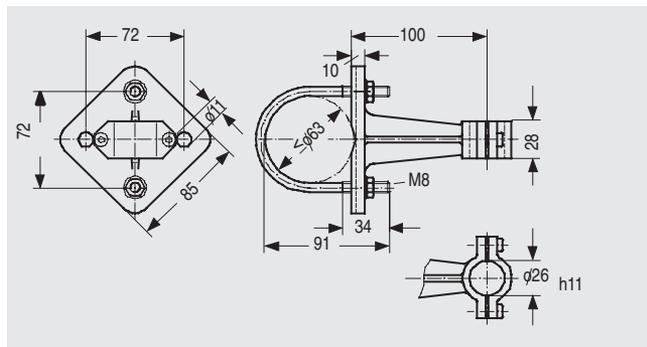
/131 Держатели измерительных приборов А, настенный или трубный монтаж, размеры
